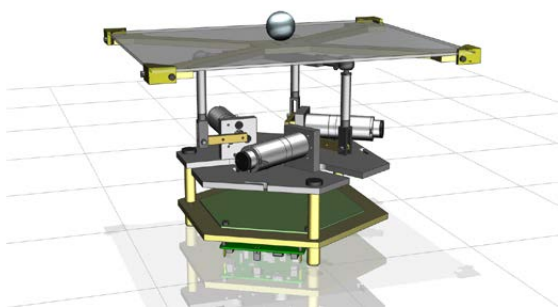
CAD Ansicht des Prototyps «Ball Balancing Platform»
